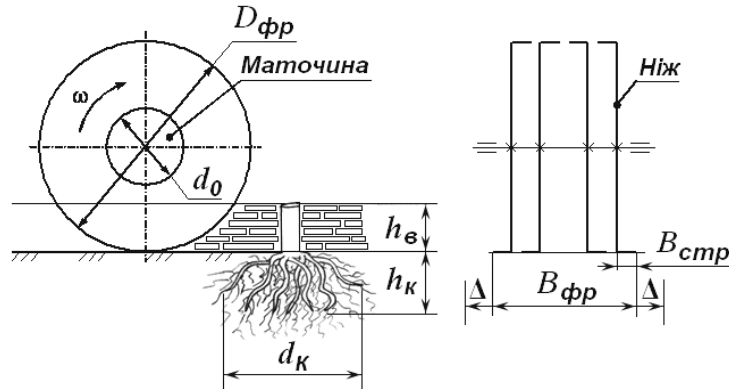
Схема технологічного обґрунтування фрезерного робочого органу
